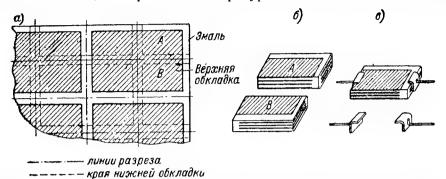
Стеклоэмалевые конденсаторы, изготовленные «мокрым» способом a — заготовка; δ — кусочки разрезанной заготовки; ϵ — припайка выводов.
